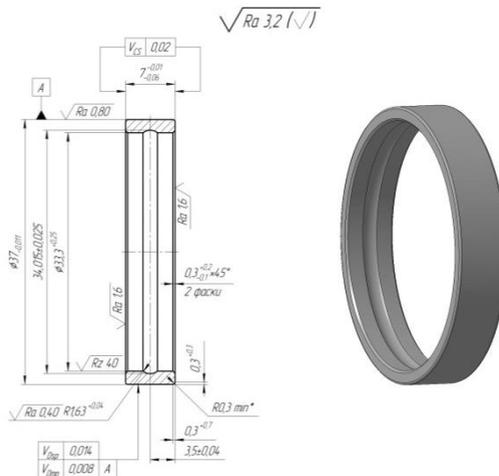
Наружное кольцо подшипника №1000805E5
